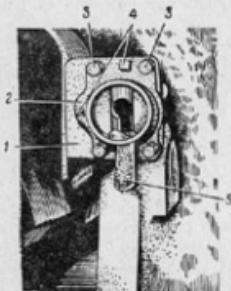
Установочное приспособление пуломета ДТ, спаренного с танковой пушкой:
